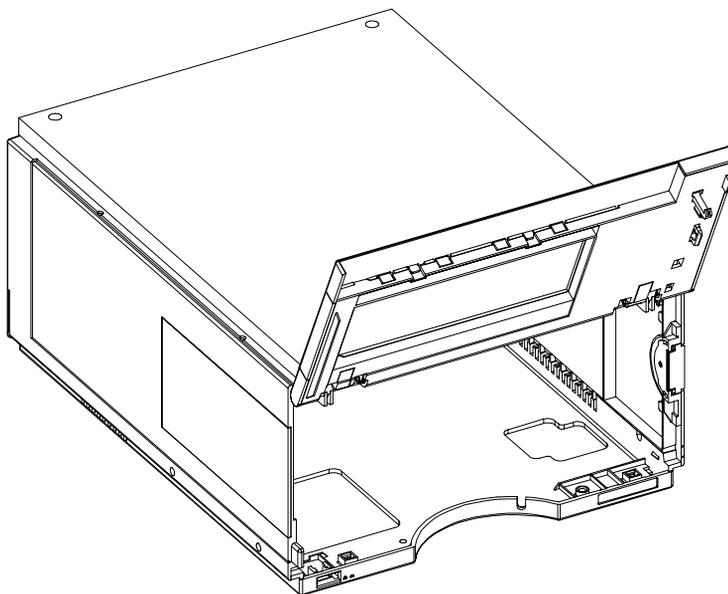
Mikro-Wellplate-Probengeber - Gehäuseteile
